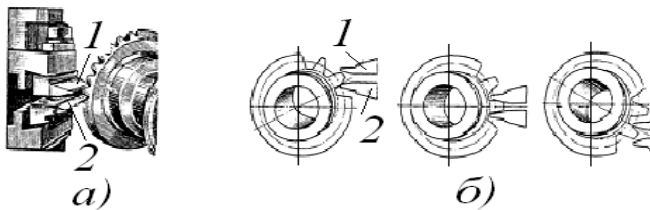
Нарізування конічного зубчастого колеса на зубостругальному верстаті:
